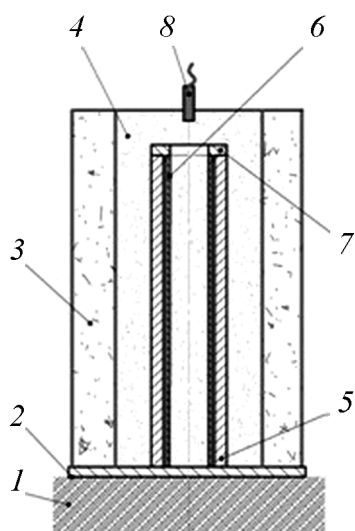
Сборка исходных элементов для сварки взрывом.
